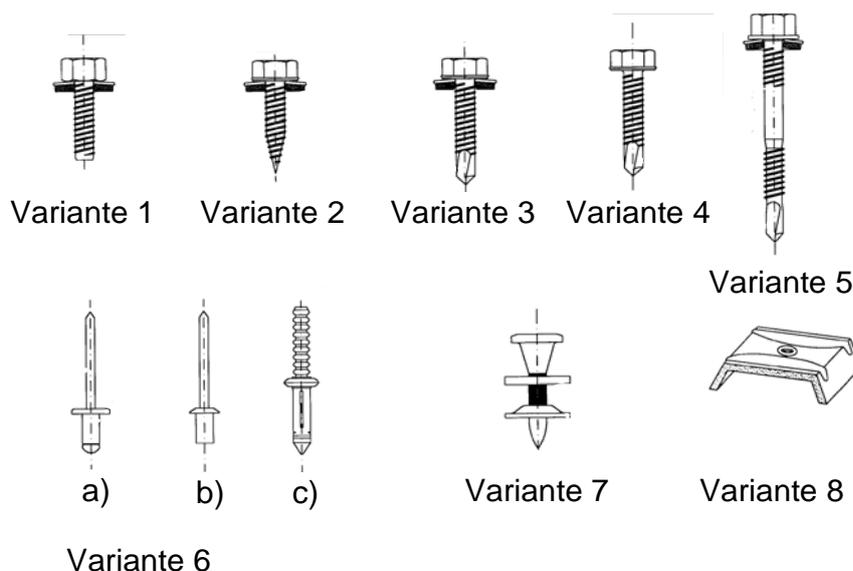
Typische Verbindungselemente für Dach und Wand im Metallbau
